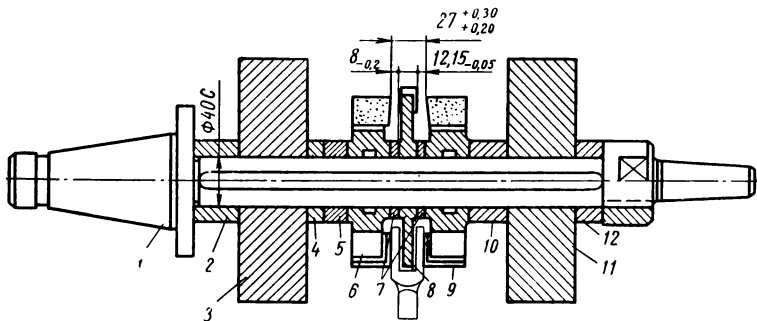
Набор твердосплавных фрез для обработки щек и прорези вилки
